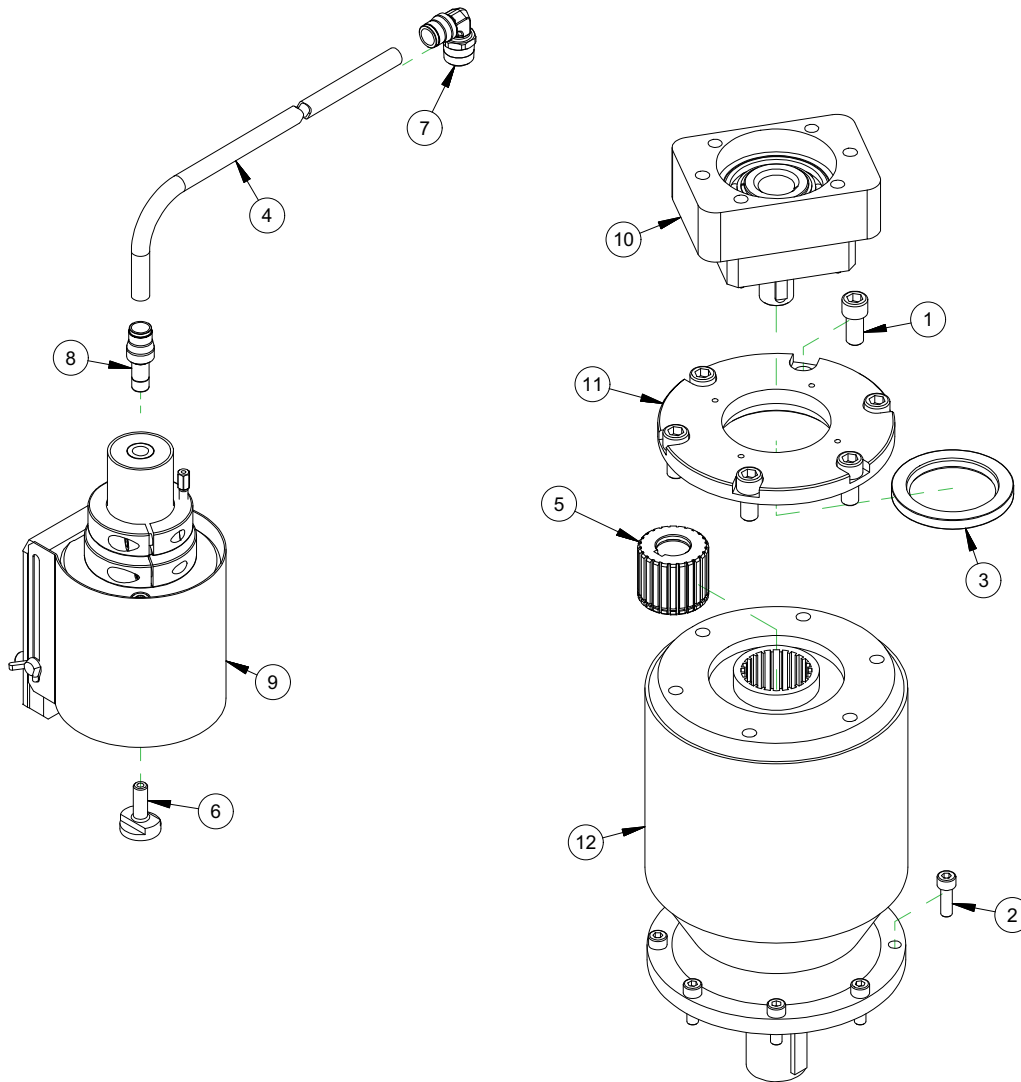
MONTAGE SUR UNE FACE (P/N 63106)
